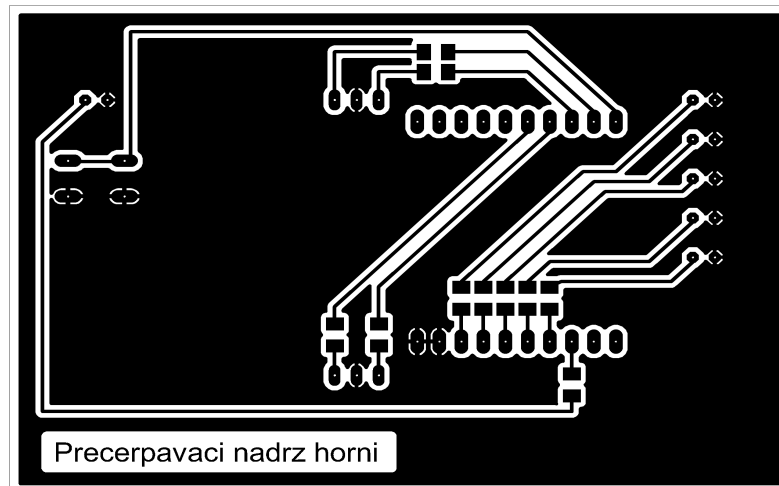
Obrazec plošného spoje spodní DPS přečerpávací nádrže
